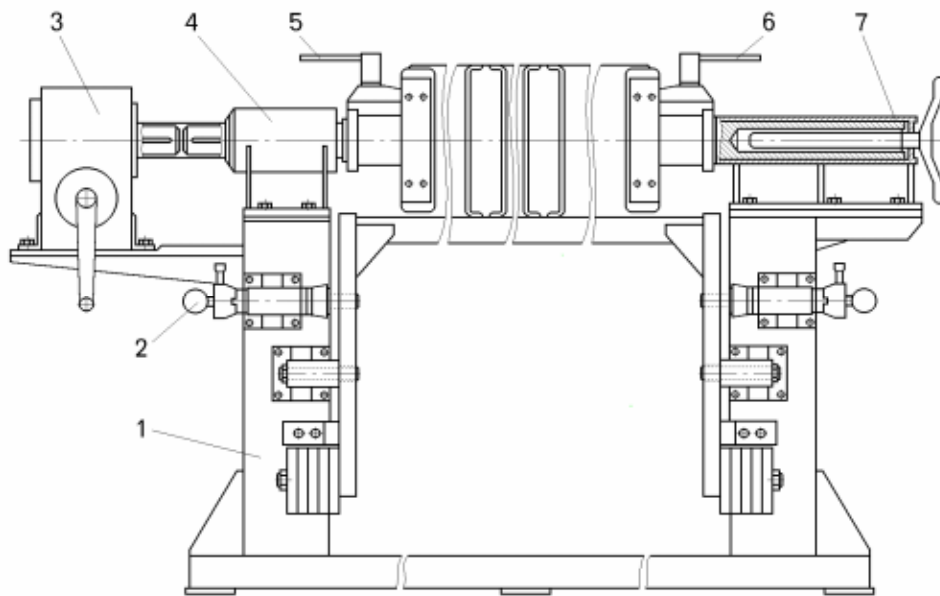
Стенд ЭСБ 11 для сборки-разборки блока радиаторов:
